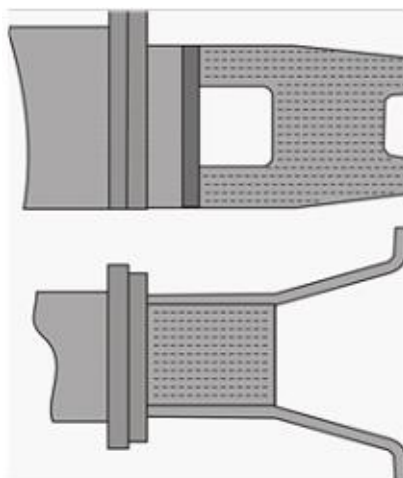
Схема сканирования основного металла корпуса тормозного блока
